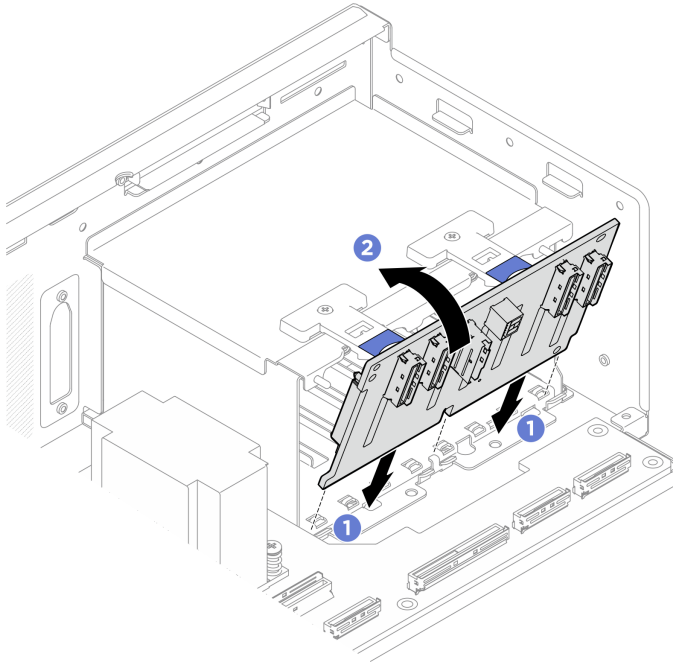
Installation d'un fond de panier d'unité 2,5 pouces
